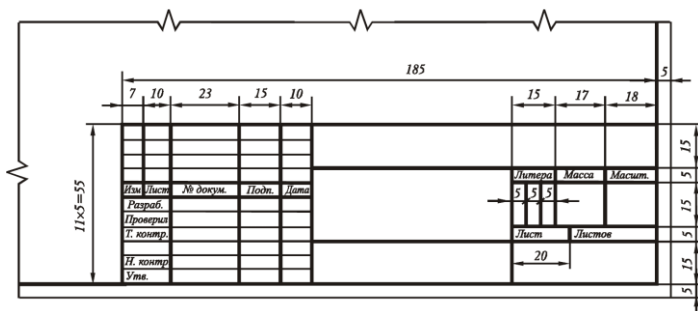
Основная надпись для чертежей и схем. Форма 1
